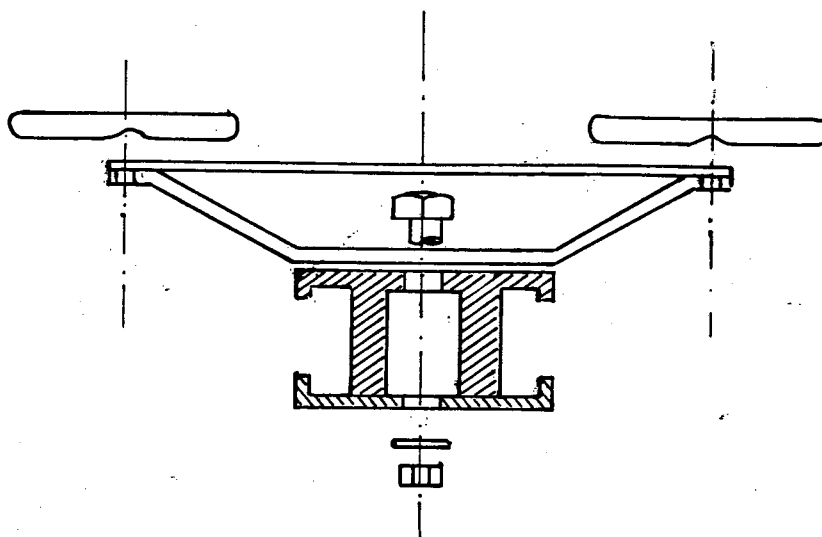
Vista dos assentos, detalhe da suporte e base de apoio para fixação no chassi [2].
